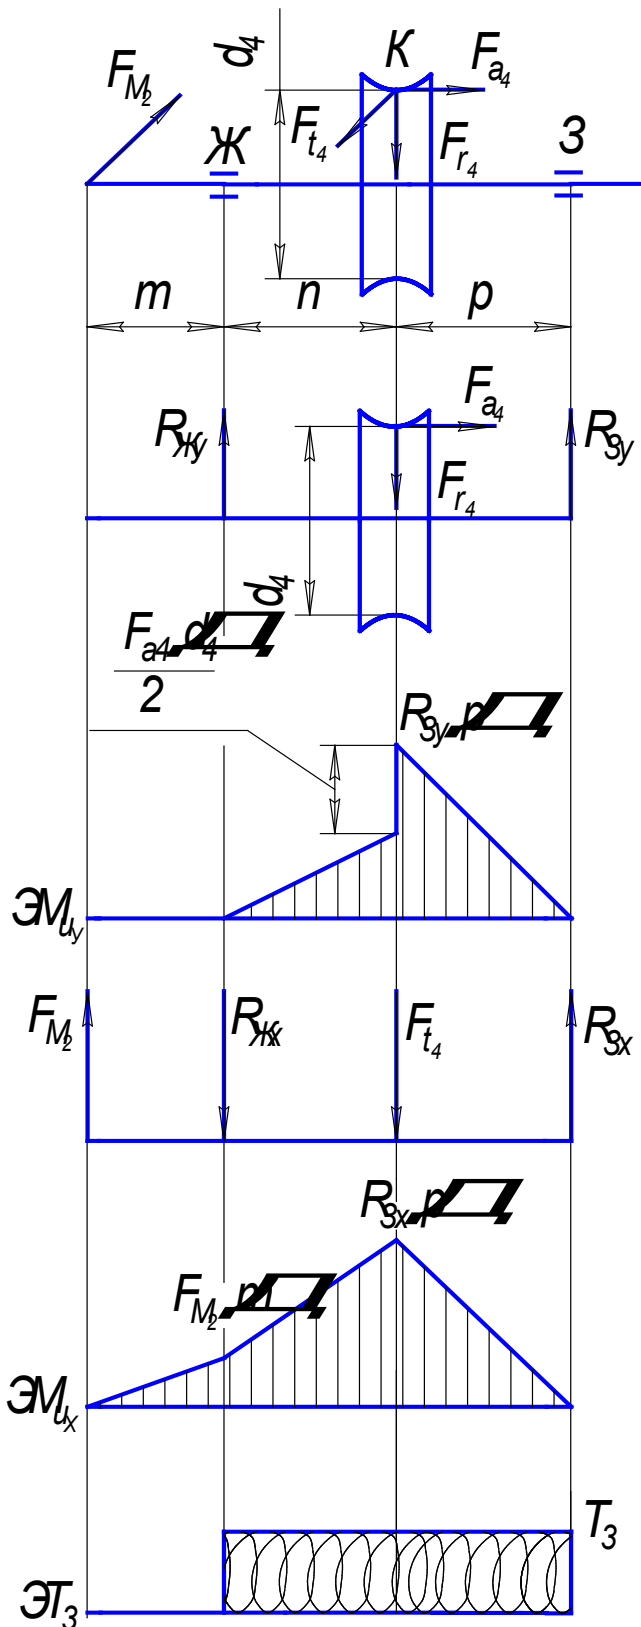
Промежуточный вал зубчато-червячного редуктора
